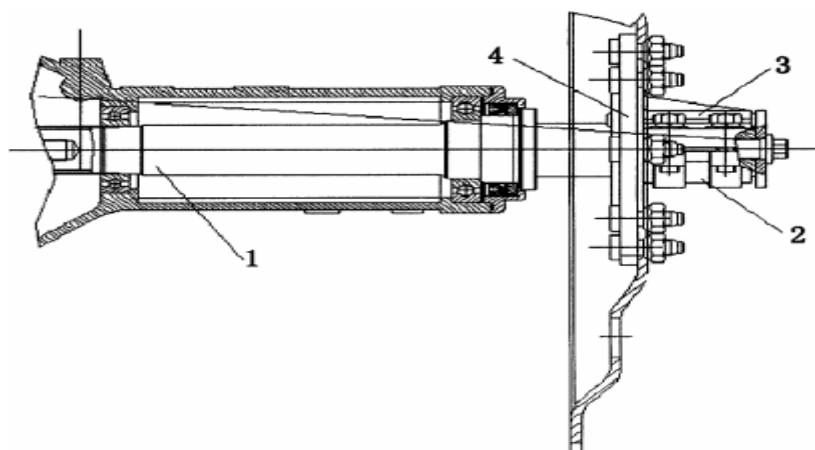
Рисунок ступенчатой регулировки протектора заднего колеса
